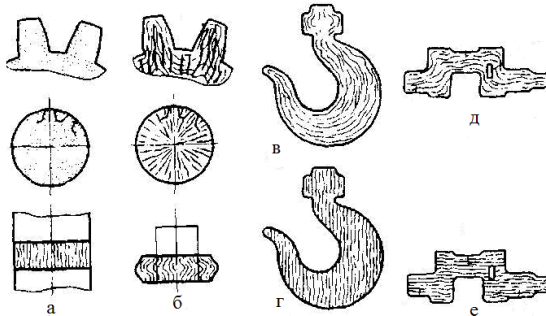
Вплив перерозподілу волокон у металі після обробки тиском : а, г, е – неправильно (лише шляхом механічної обробки заготовки); б, в, д – правильно (шляхом попереднього пластичного деформування заготовки)
